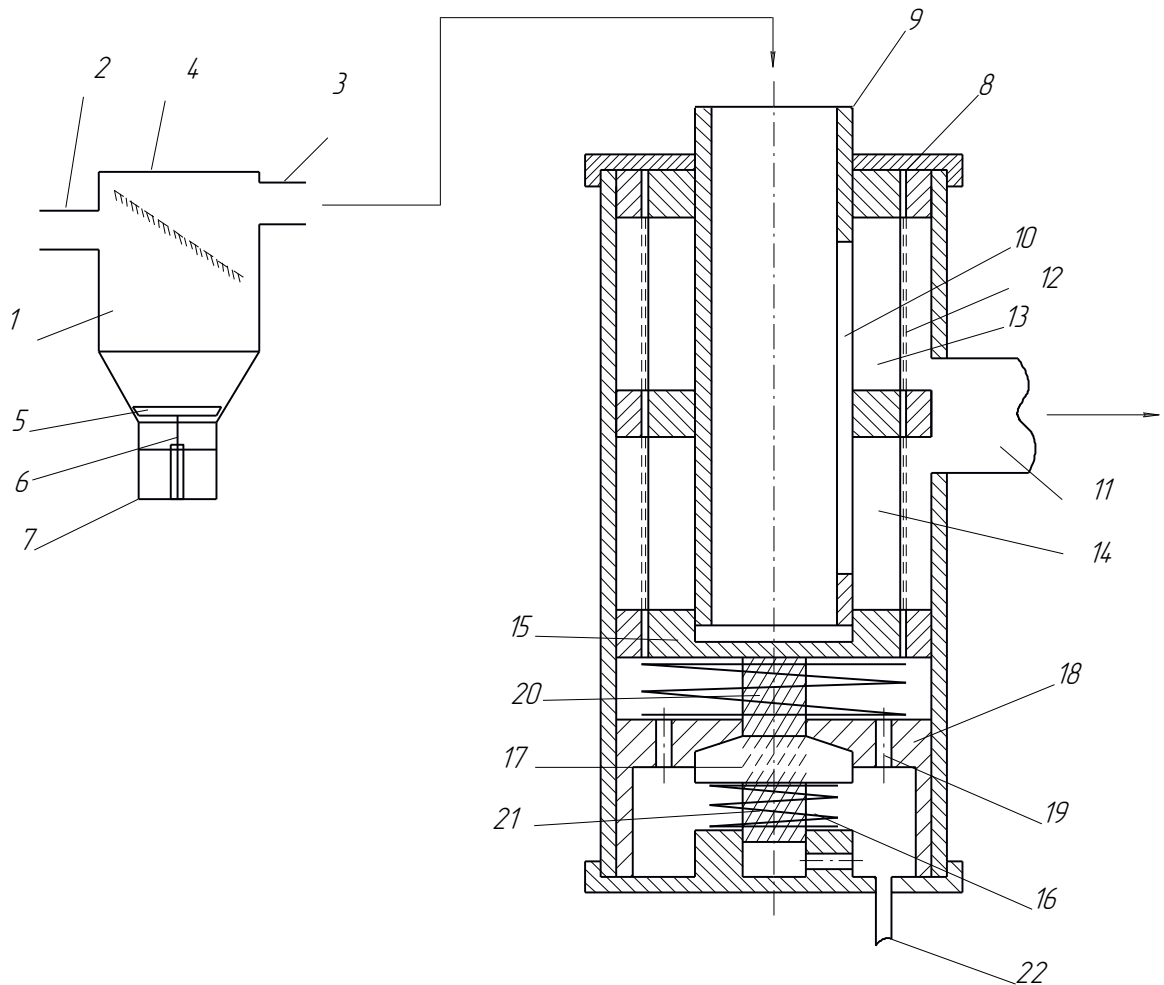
Схема молочного фільтру : 1-приймач молока; 2-вхідний патрубок; 3-вихідний патрубок; 4-фільтр грубого очищення; 5-конусна пробка; 6-шток; 7-відстійник; 8-корпус; 9-циліндрична камера; 10-бічна щілина; 11-вихідний патрубок; 12-фільтруючий елемент; 13-біляче колесо; 14-ребро бічне; 15-поршень; 16-хвостик; 17-гайка; 18-опорна втулка; 19-направляючі отвори; 20,21-пружина; 22-зливний отвір.
